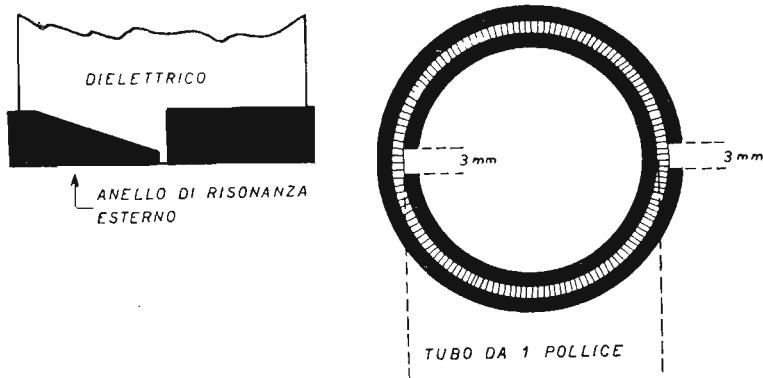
Dimensioni del circuito a split-ring per ondametro UHF.
